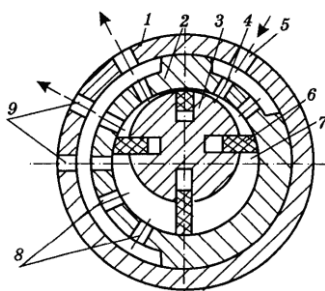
Пневмодвигун: 1 – корпус; 2 – статор; 3 – ротор; 4, 8 – отвори у статорі; 5, 9 – отвори у корпусі; 6 – пластини; 7 – камера
